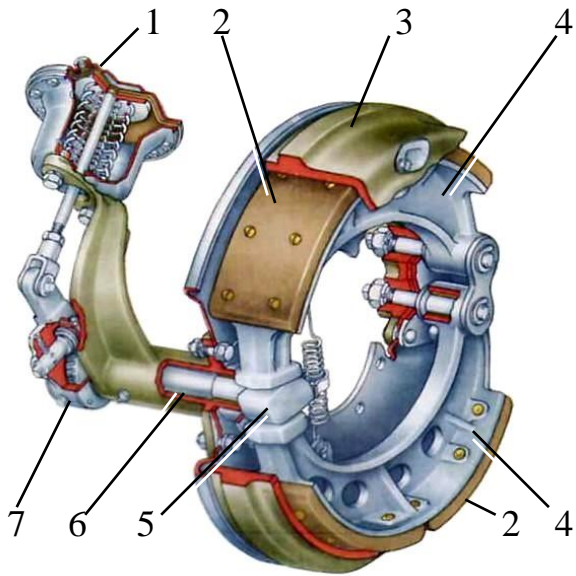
Барабанный тормозной механизм с кулачковым разжимным устройством: 1 – исполнительный механизм тормозного привода; 2 – накладки тормозных колодок; 3 – тормозной барабан; 4 – тормозные колодки; 5 – кулачок разжимного устройства; 6 – вал кулачка; 7 – регулировочный механизм
